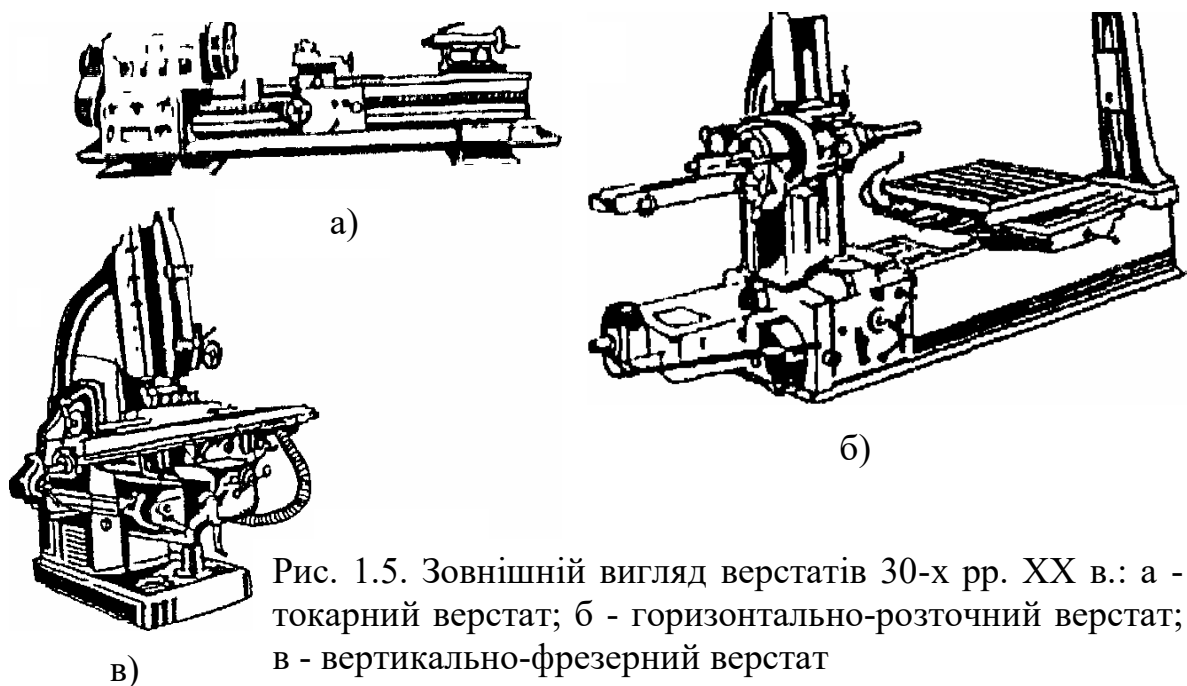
Зовнішній вигляд верстатів 30-х рр. XX в.: а - токарний верстат; б - горизонтально-розточний верстат; в - вертикально-фрезерний верстат
